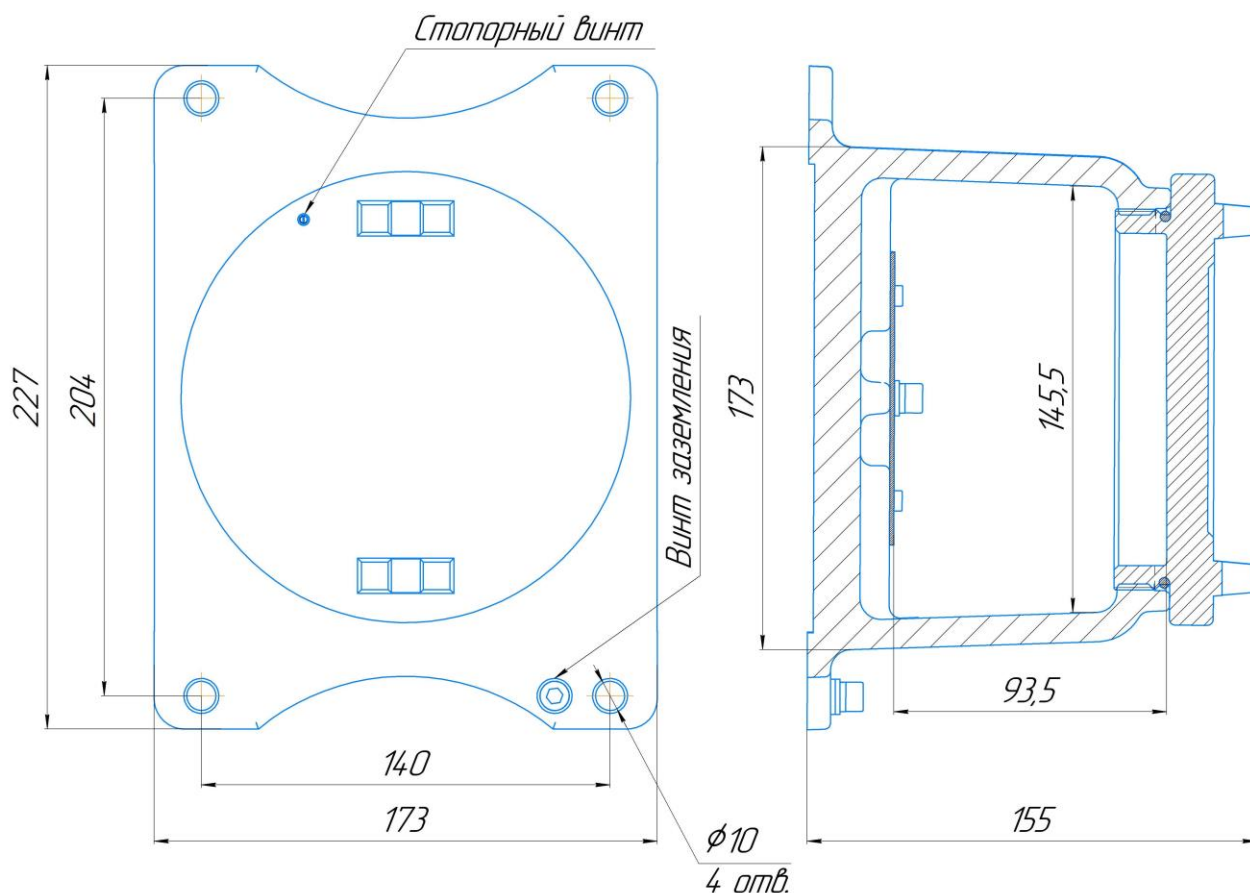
Внешний вид и габаритные размеры Спектрон-ККВ-Exd-A
